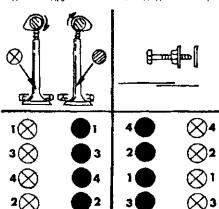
Регулировка зазоров клапанов, когда закрыты клапаны цилиндров, указанных слева. Регулируются зазоры клапанов цилиндров, указанных справа.
